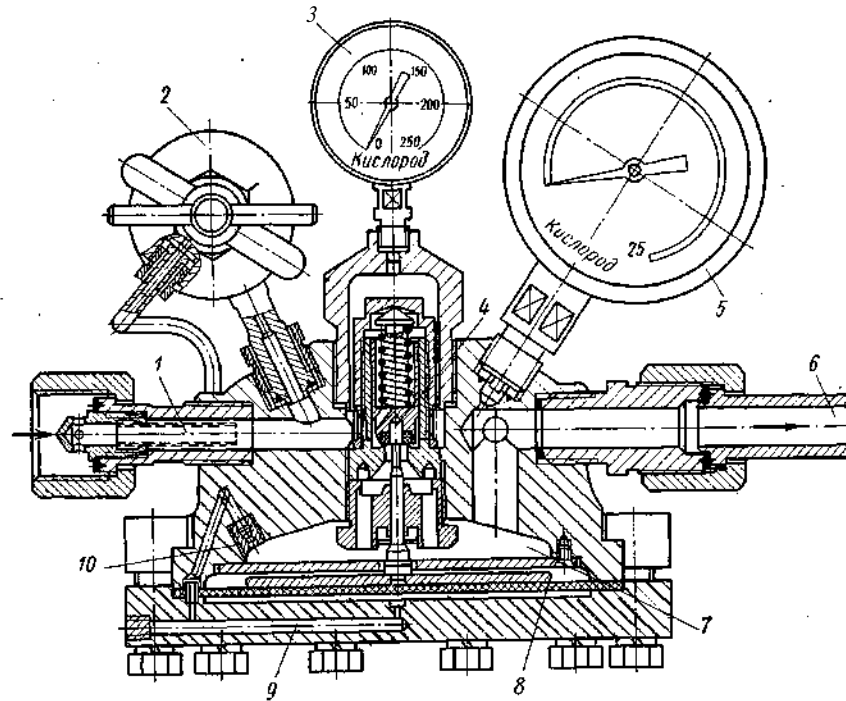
Рамповый редуктор ДКР-250/500 с пневматическим заданием величины рабочего давления:
